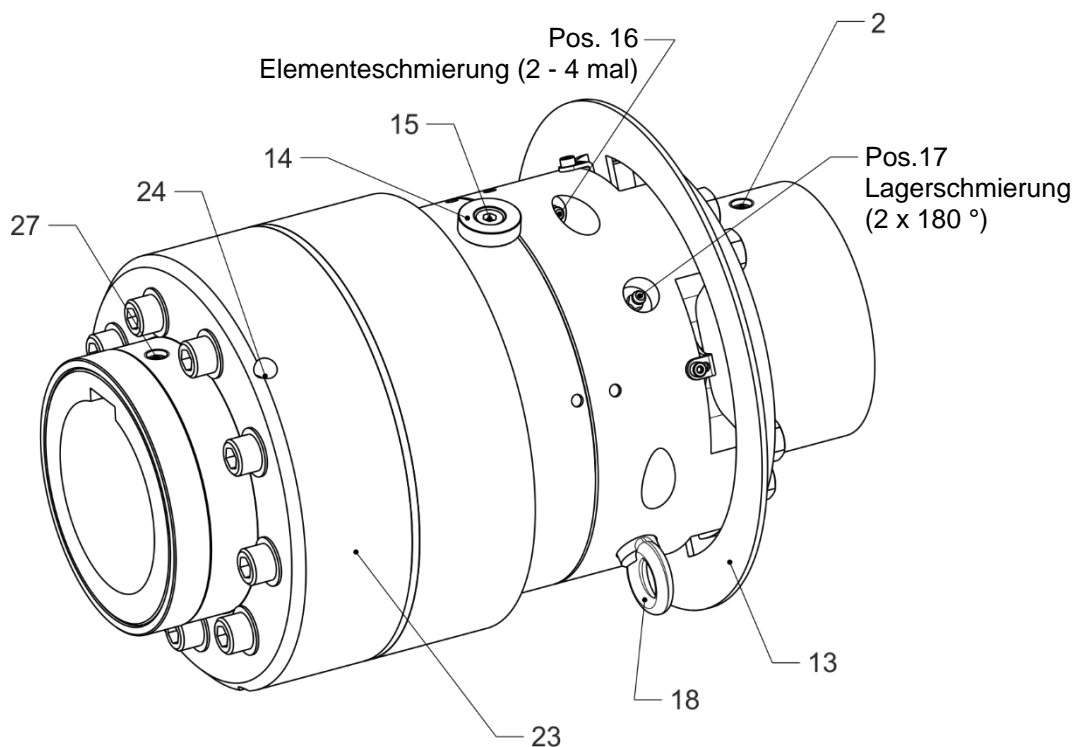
Type 4043._1400 (Ausführung mit Schaltscheibe (13))
